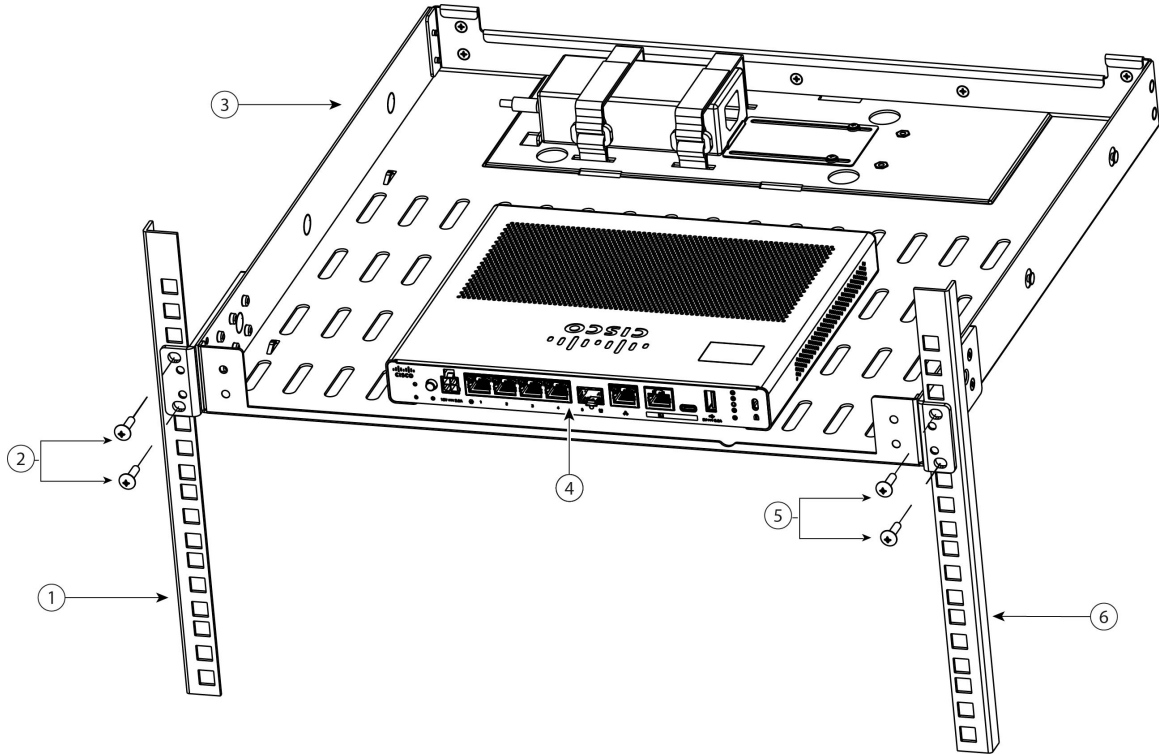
Instale los soportes de gestión de cables en el estante de montaje en rack
